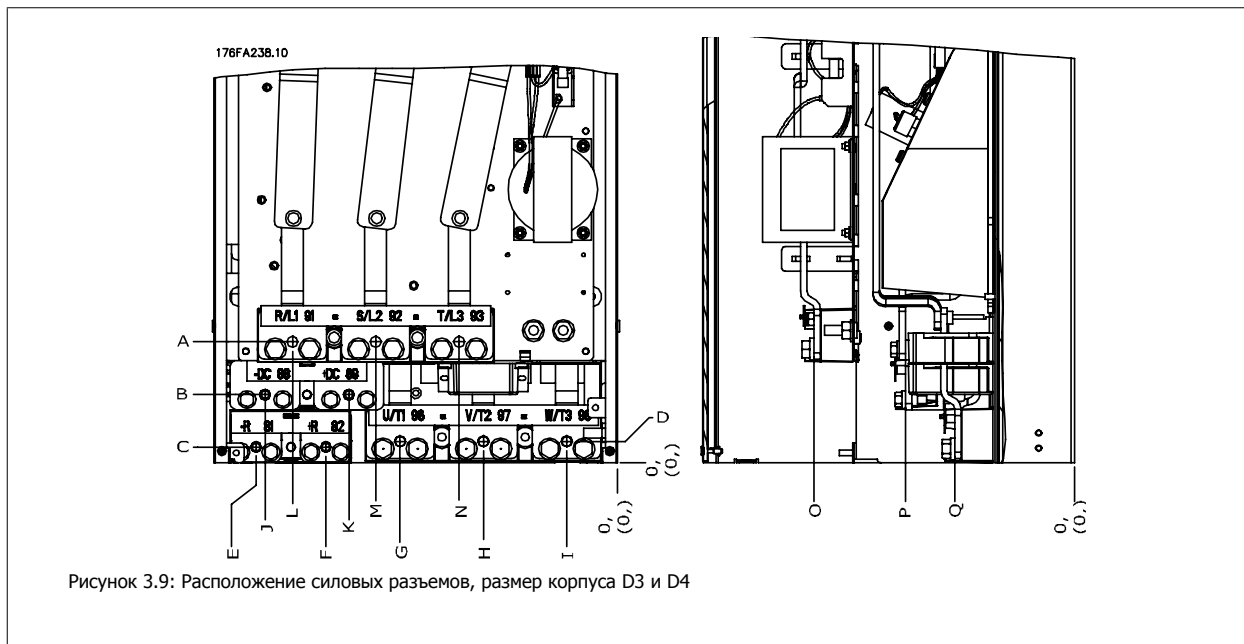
Расположение силовых разъемов, размер корпуса D3 и D4
